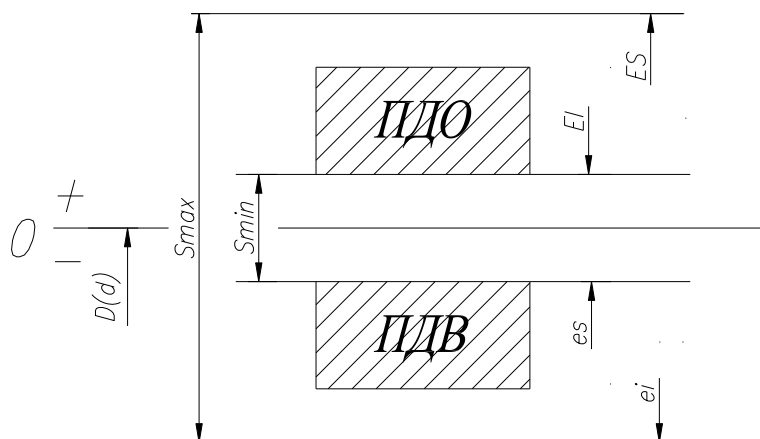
Схема розташування полів допусків з'єднання з зазором
